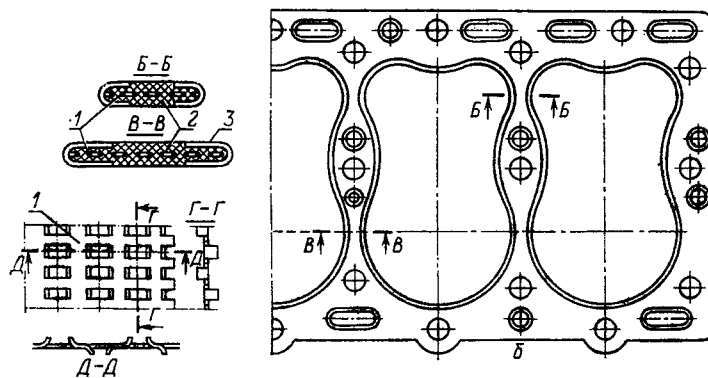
Прокладка головки цилиндров двигателя ГАЗ-52:
